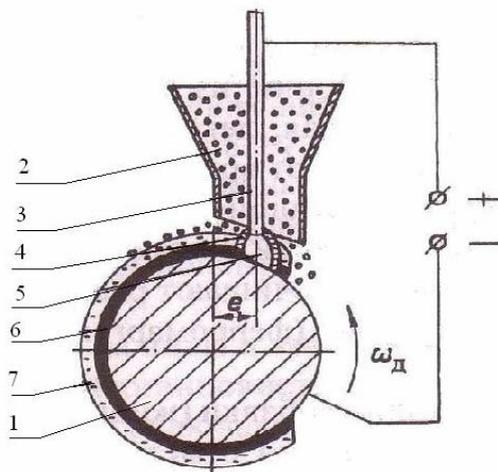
Наплавка цилиндрической детали под слоем флюса:
